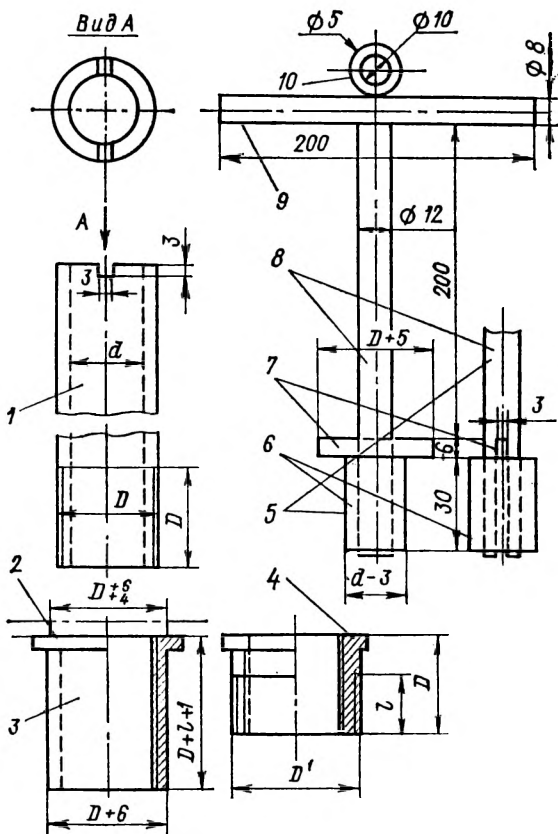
Заналичная труба, ниппель для ее крепления и ключ для ее заворачивания:  $d$  — номинальный внутренний диаметр заналичной трубы и трубной резьбы на ней;  $D$  — наружный диаметр трубной резьбы (фактический) на заналичной трубе;  $D'$  — номинальный диаметр трубной резьбы на наружной поверхности укороченного ниппеля;  $l$  — длина резьбы для фиттинга на диаметре  $D$ ;
